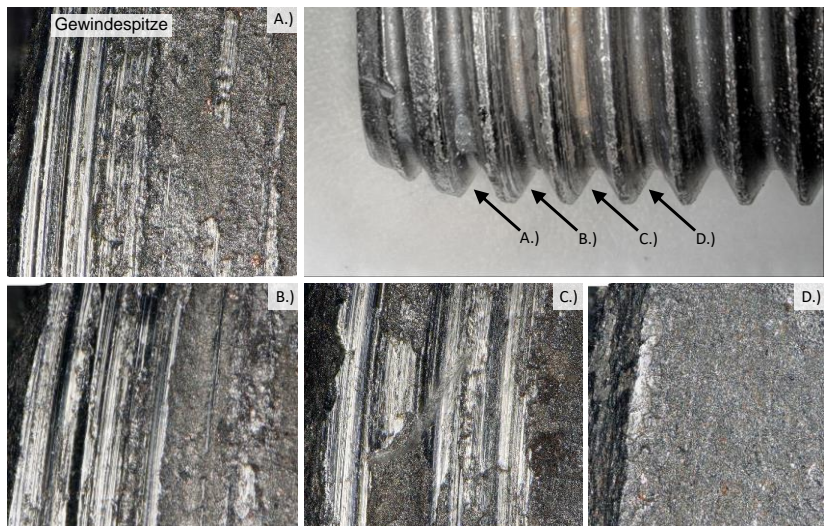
Gewindefläche einer manuell angezogenen Schraube
